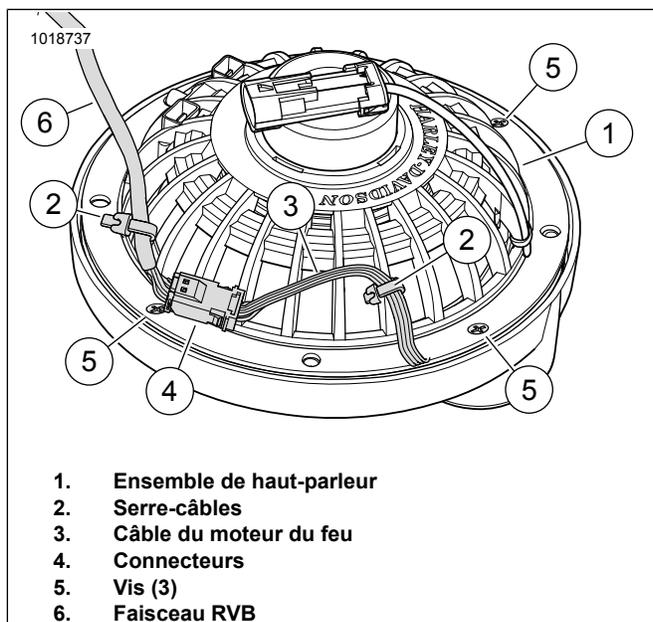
Arrière du haut-parleur, câble et serre-câbles
